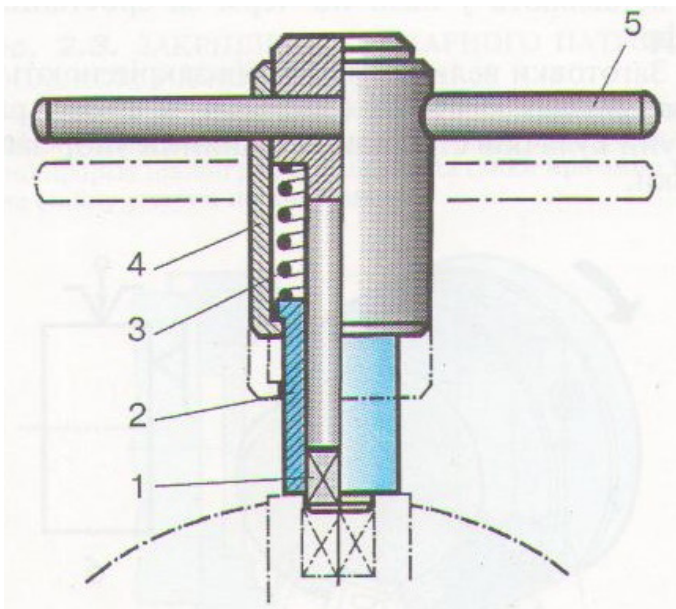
Самовідкидний безпечний ключ до токарного патрона:
